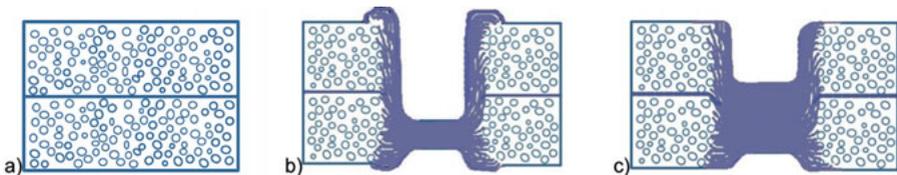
a) Zwei Materiallagen vor dem Verschweißen; b) schlechte Schweißnaht; c) gute Schweißnaht
